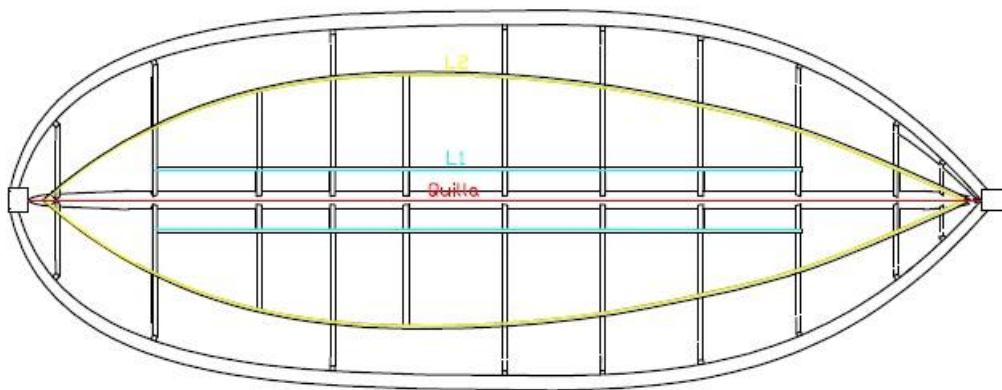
Refuerzos longitudinales (Fuente: elaboración propia)
